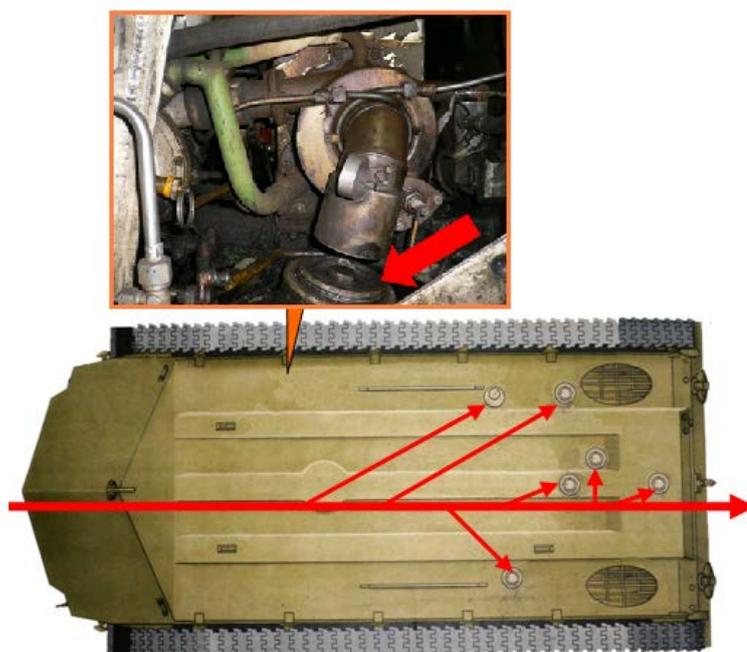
Проверка установки и затяжки лючков и пробок днища при КО БМД-2
